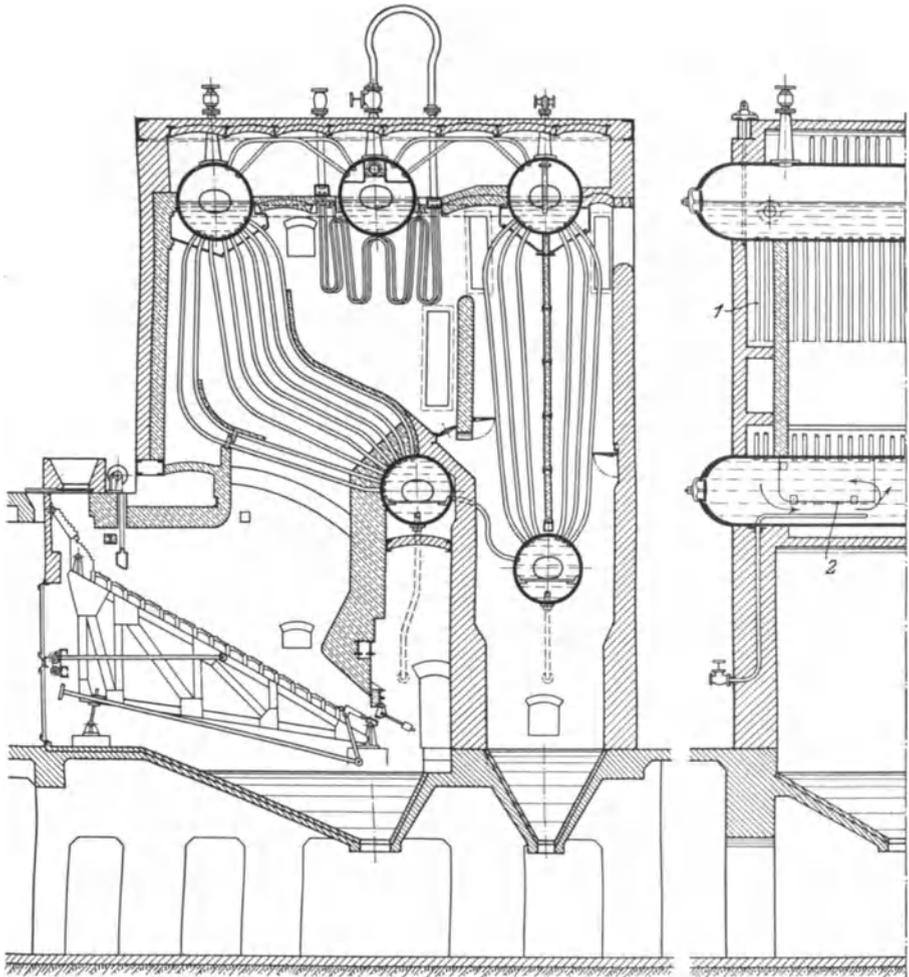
u. 34. Höchstdruckteilerrohrkessel mit mechanischem Vorschubrost für Braunkohle der Firma L. u. C. Steinmüller, Gummersbach.
